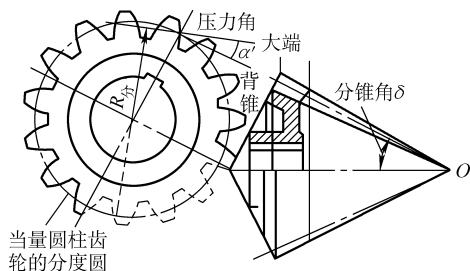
选择锥齿轮铣刀的当量圆柱齿轮
